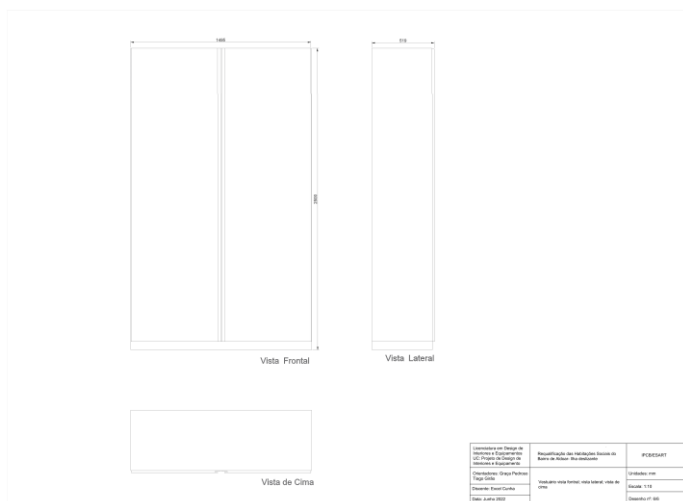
Desenho técnico de conjunto de vestuário 150 cm.
